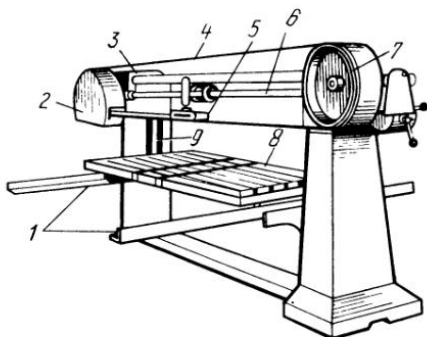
Ленточный шлифовальный станок ШЛПС:
